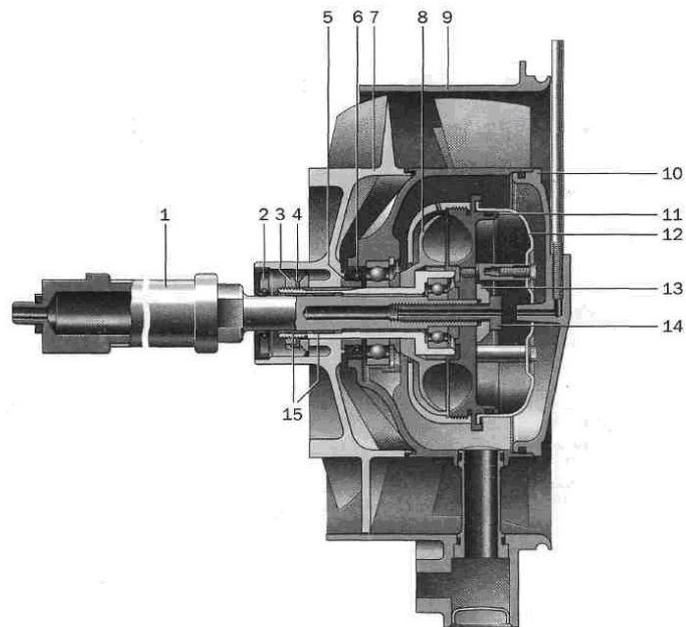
Установка гидравлической муфты в приводе вентилятора: 1 — вал привода вентилятора; 2, 6 — сальники (манжеты); 3 — гайка вала; 4 — стопорная шайба; 5 — втулка сальника; 7 — рабочее колесо; 8 — гидромуфта; 9 — корпус вентилятора; 10 — крышка; 11 — уплотнительное кольцо; 12 — корпус центрифуги; 13 — шайба; 14 — маслопроводный болт; 15 — подшипник скольжения
